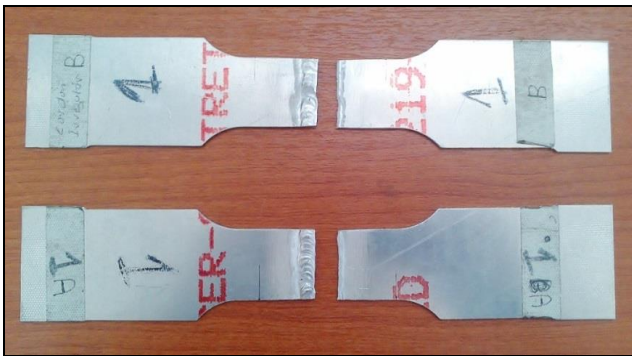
Detalle de rotura en zona afectada por el calor en probetas de tracción ensayadas.
